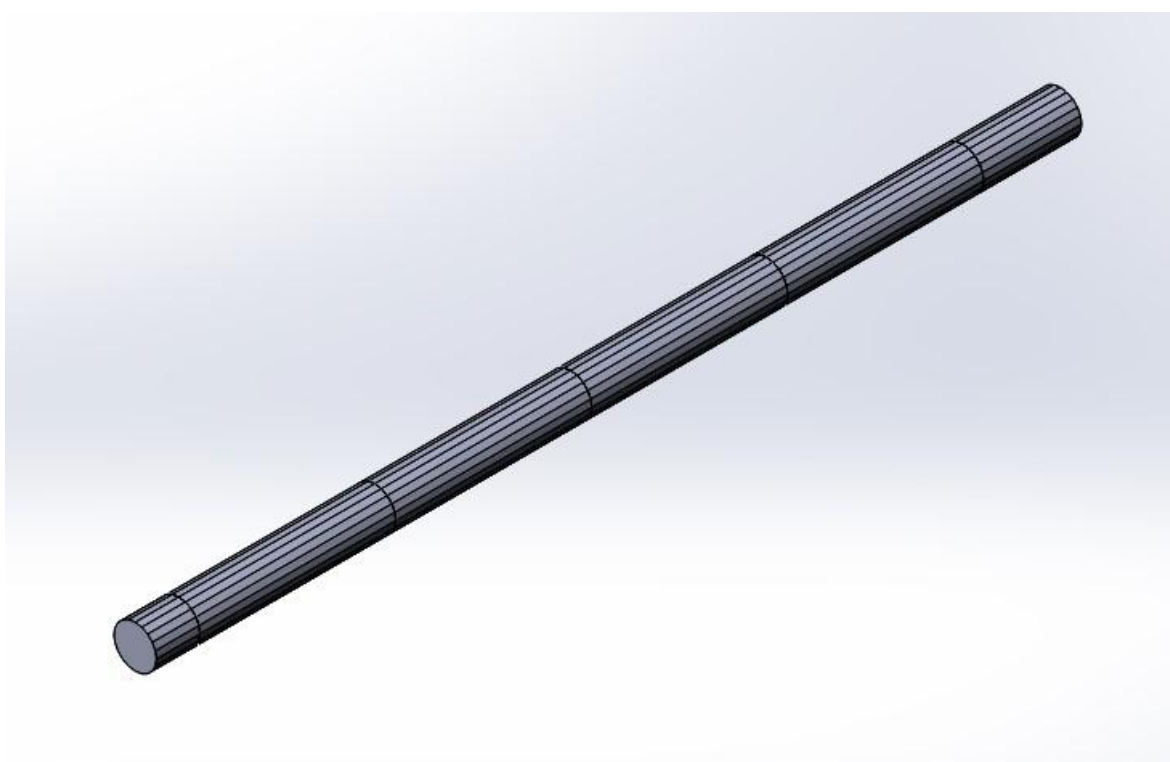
Пресована вуглецева заготовка (фрагмент)
